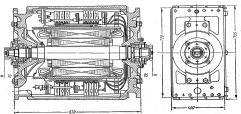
Габаритные размеры электродвигателя типа МАД 191/11 мг
